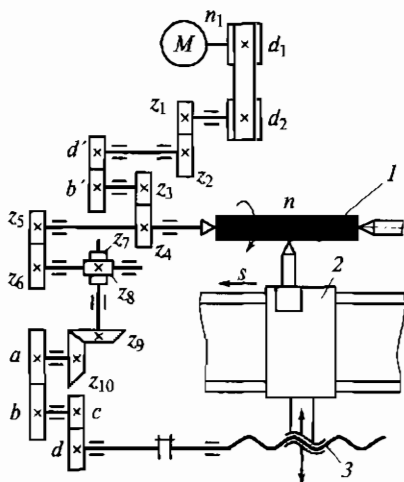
Упрощенная кинематическая схема токарно-винторезного станка:
